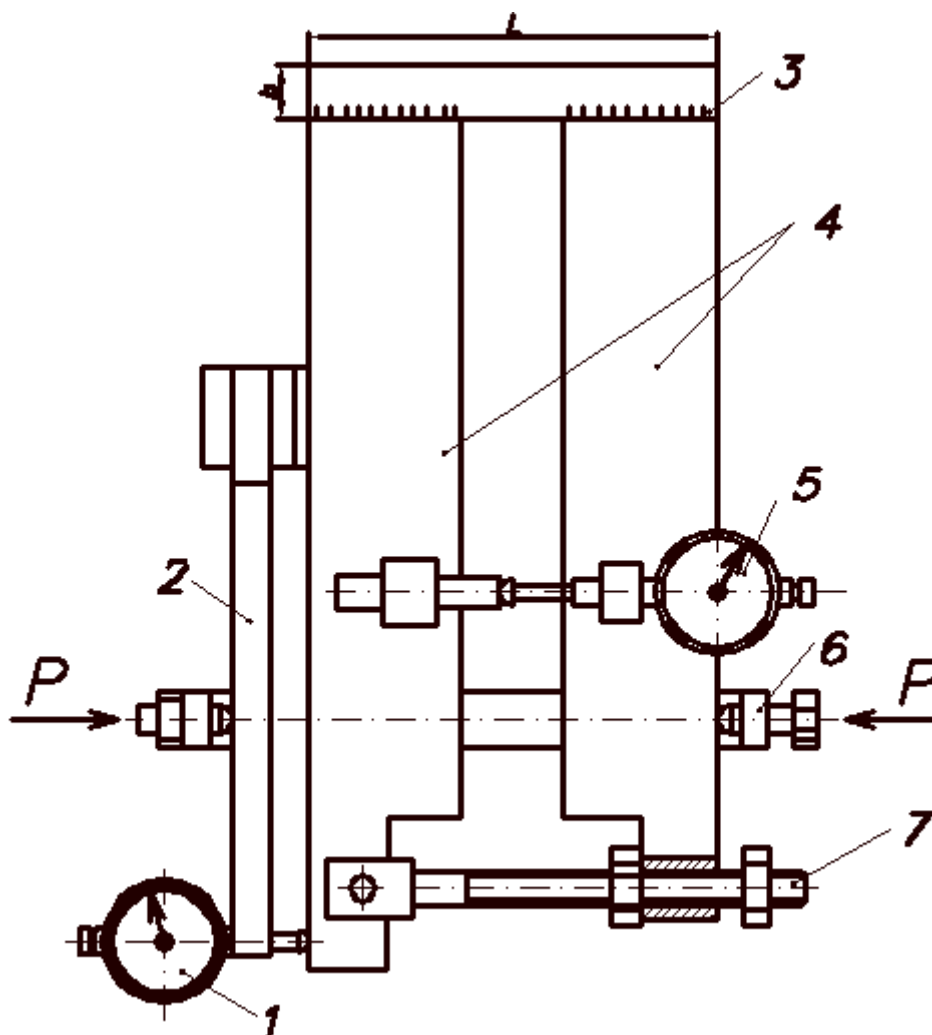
Схема устройства для испытания образцов: 1-индикатор для измерения прогиба консоли упругого элемента; 2-упругий элемент; 3-образец; 4-левая и правая стойки; 5-индикатор для измерения перемещений; 6-съемная струбцина; 7-винтовой фиксатор.
